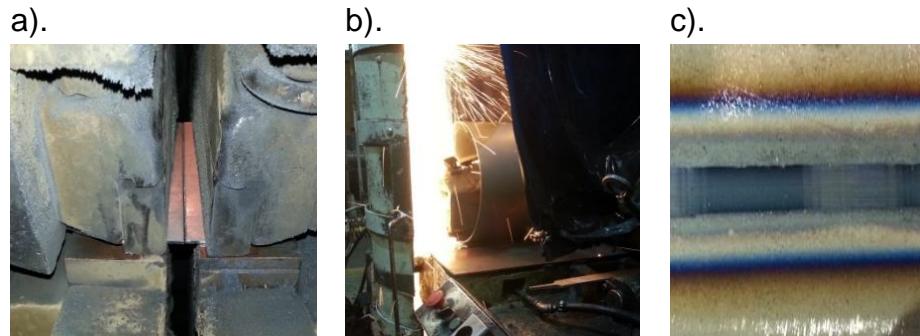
Realización de uniones soldadas. a) Junta lista para ser soldada, b) Ejecución de la operación de soldadura, c) Junta soldada
